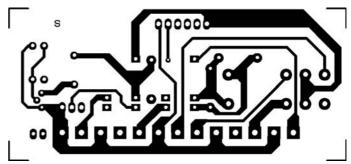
Dessin, à l'échelle 1, du côté "soudures" du circuit imprimé double face de la platine des I/O de l'antivol domestique à deux zones.
